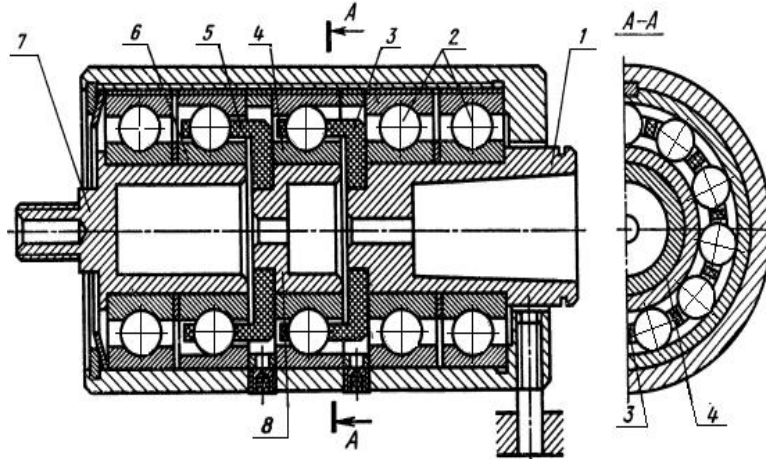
Двухступенчатый шариковый планетарный мультипликатор
